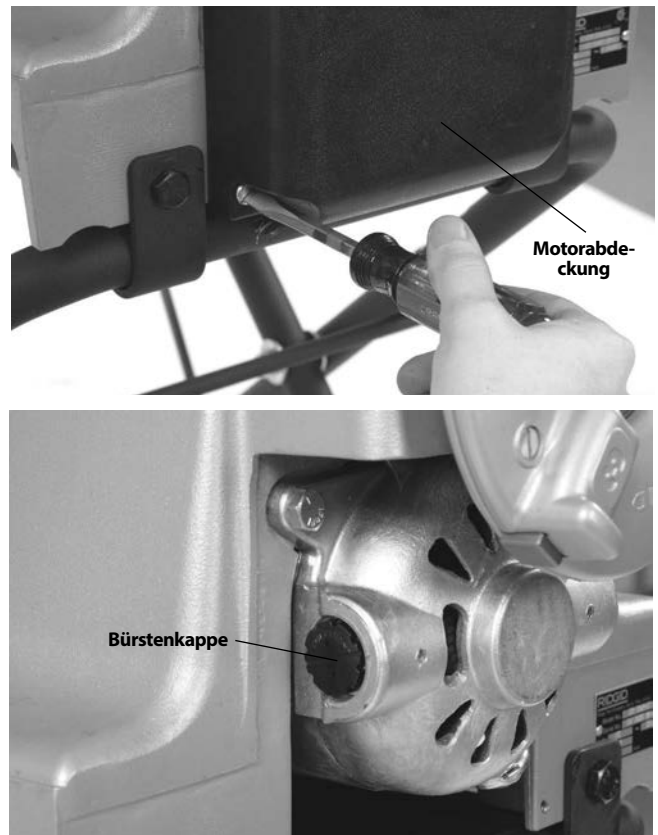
Entfernen der Motorabdeckung/Wechseln der Bürsten
